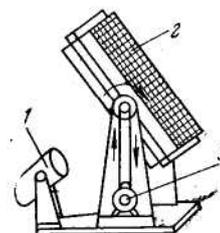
Приспособление для сушки сотопластов: 1 – вентилятор; 2 – сотопласт; 3 – электродвигатель
